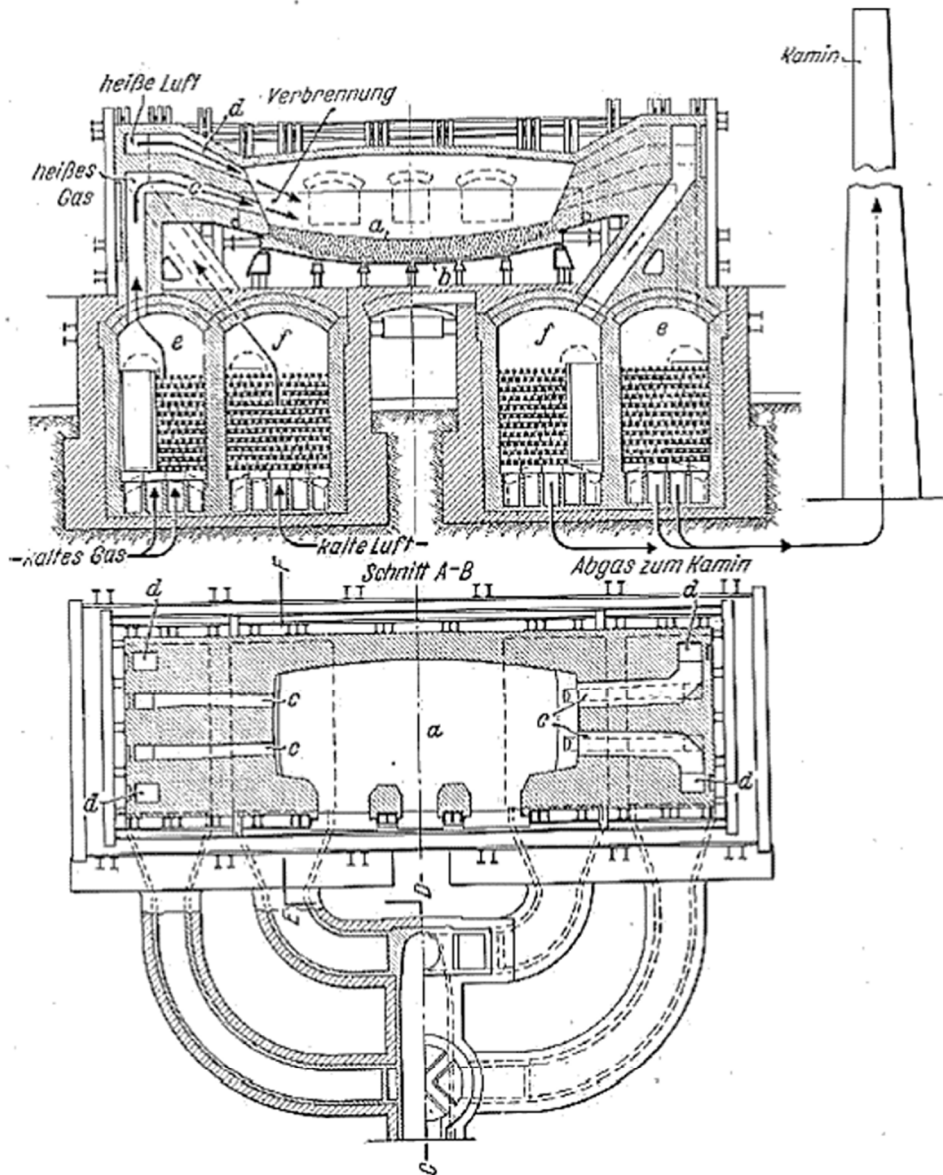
und Abbildung 2-11 zeigen einen Siemens Martin Ofen im Längs- und Querschnitt. Er besteht aus einem Herd, der auf starke gusseiserne Herdplatten (b) aufgestampft wird. Wobei das Futter basisch oder sauer sein kann. Das basische Futter ist reich an Dolomit, wo hingegen das saure Futter aus Kieselsäure besteht. Es münden mehrere Kanäle (c und d), welche Züge genannt werden, in den Ofen. Diese stellen eine
